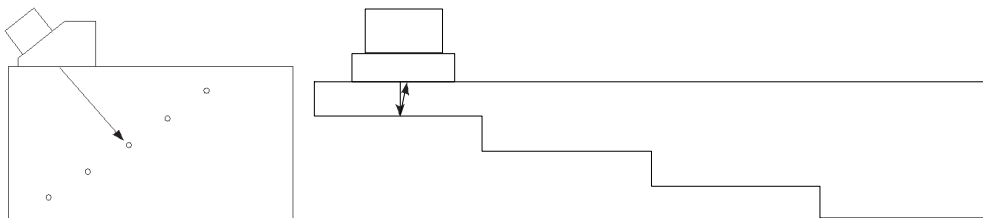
Калибровочные образцы для калибровки кривой ДАС
